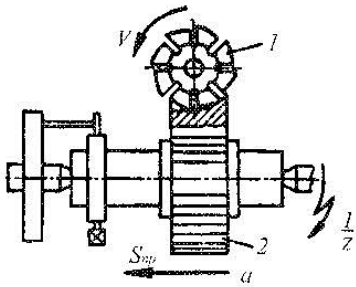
Схеми фрезерування зубів за методом копіювання
